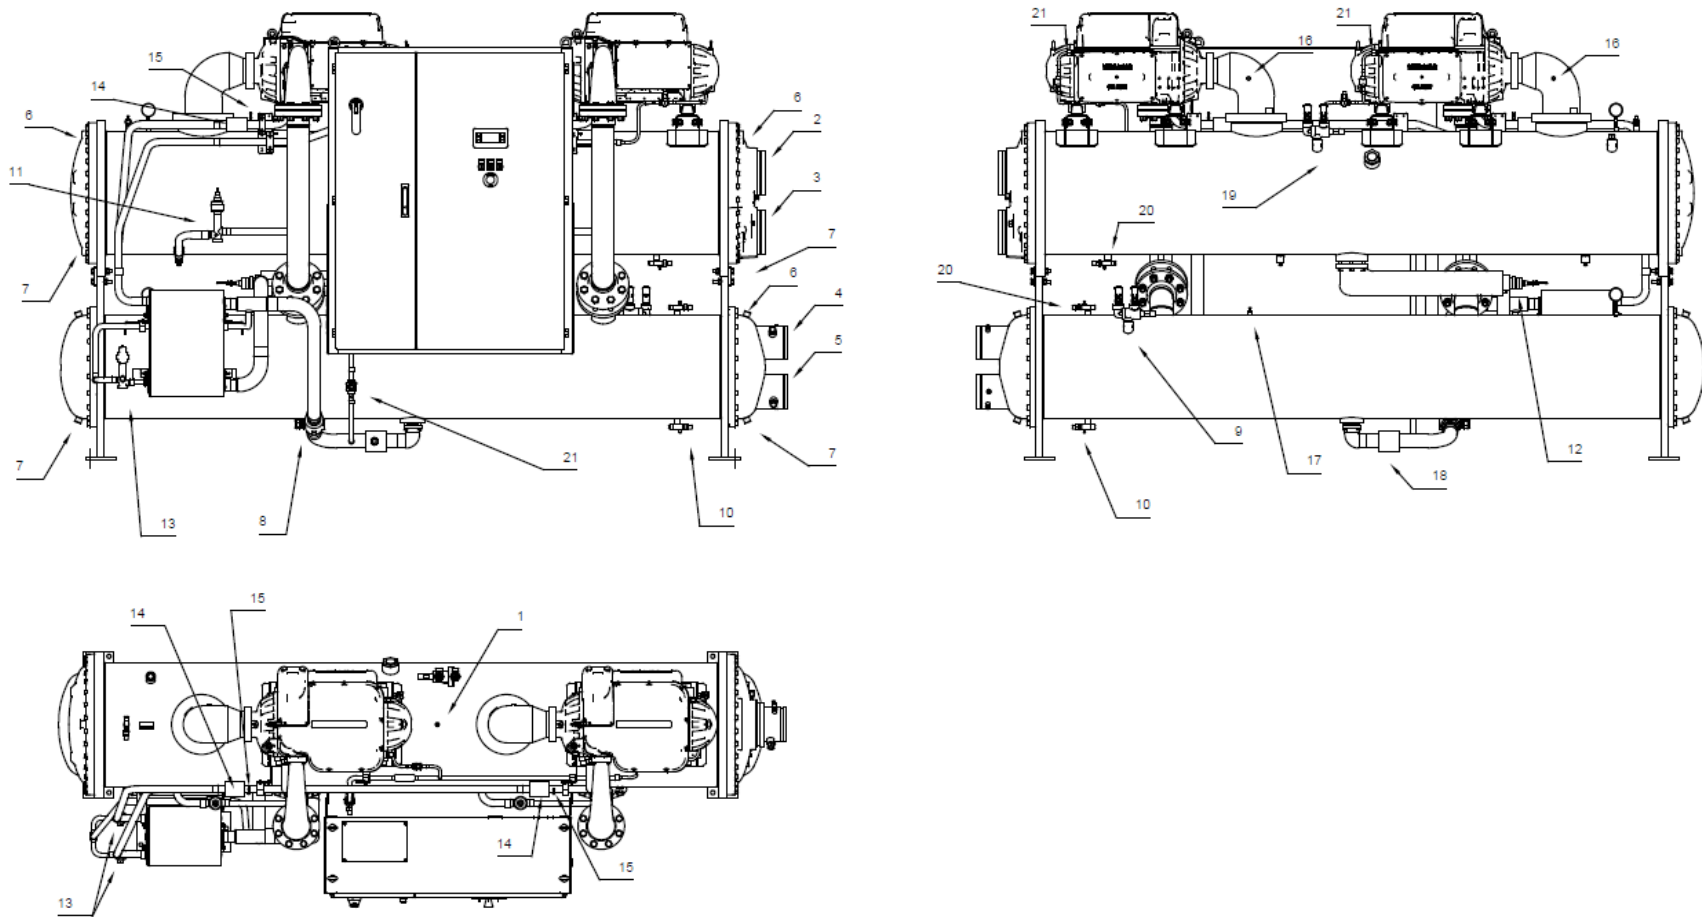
Descripciones del componente de la unidad del compresor doble
